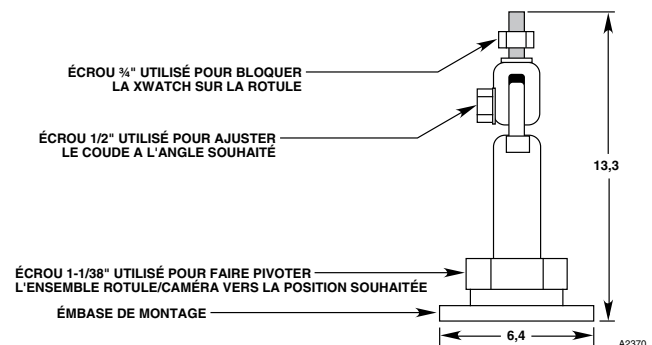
Dimensions du Support de Montage à Rotule en Inox Q9001H (en Centimètres)
